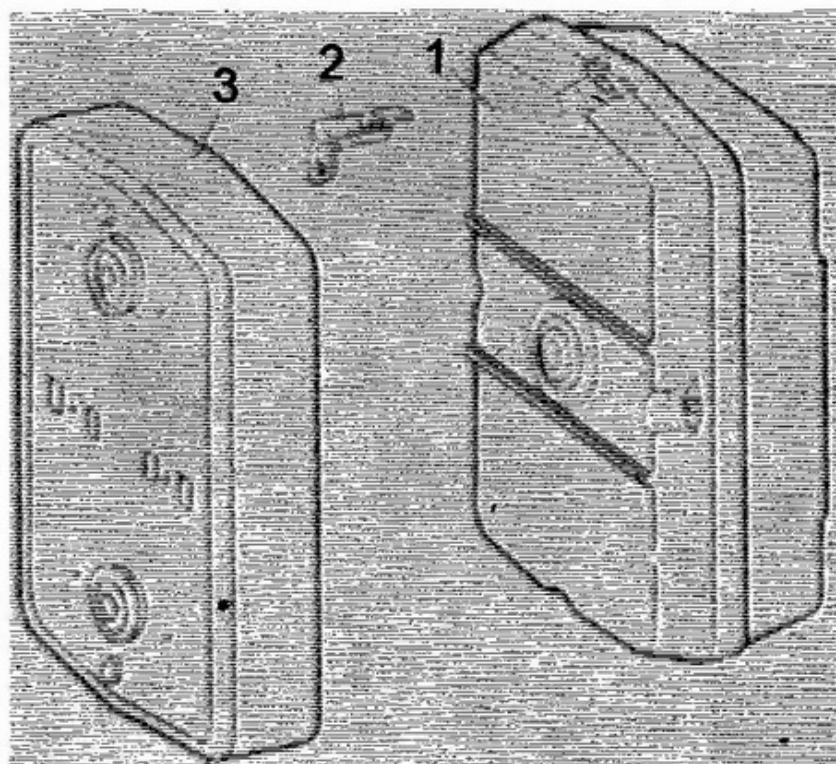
Установка светомаскировочной насадки АС132 на задний фонарь:
